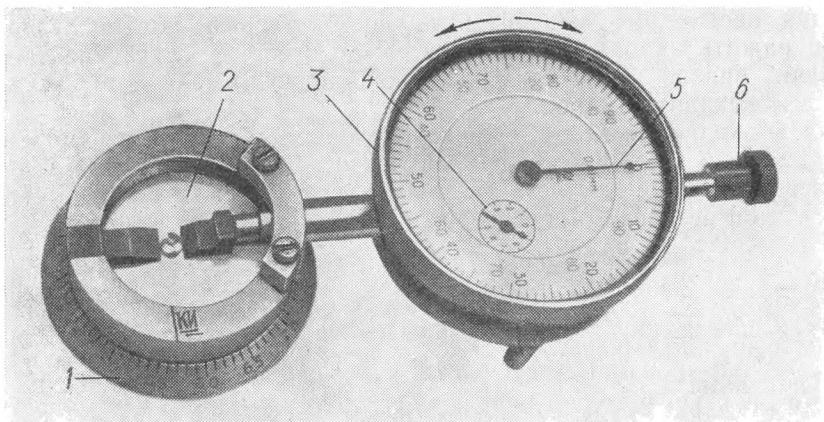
Приспособление для контроля за диаметром полуфабриката.
